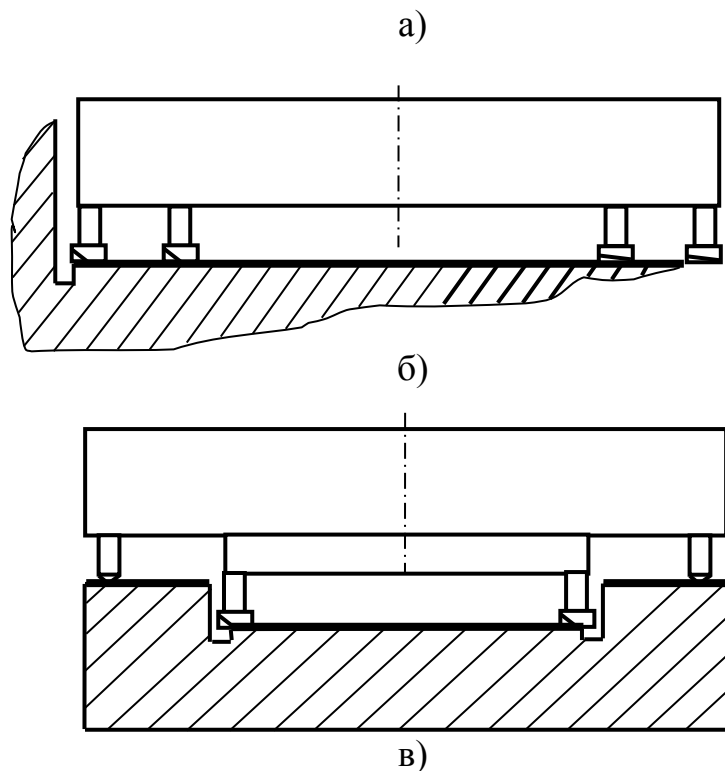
Схеми обробки плоских поверхонь деталей
